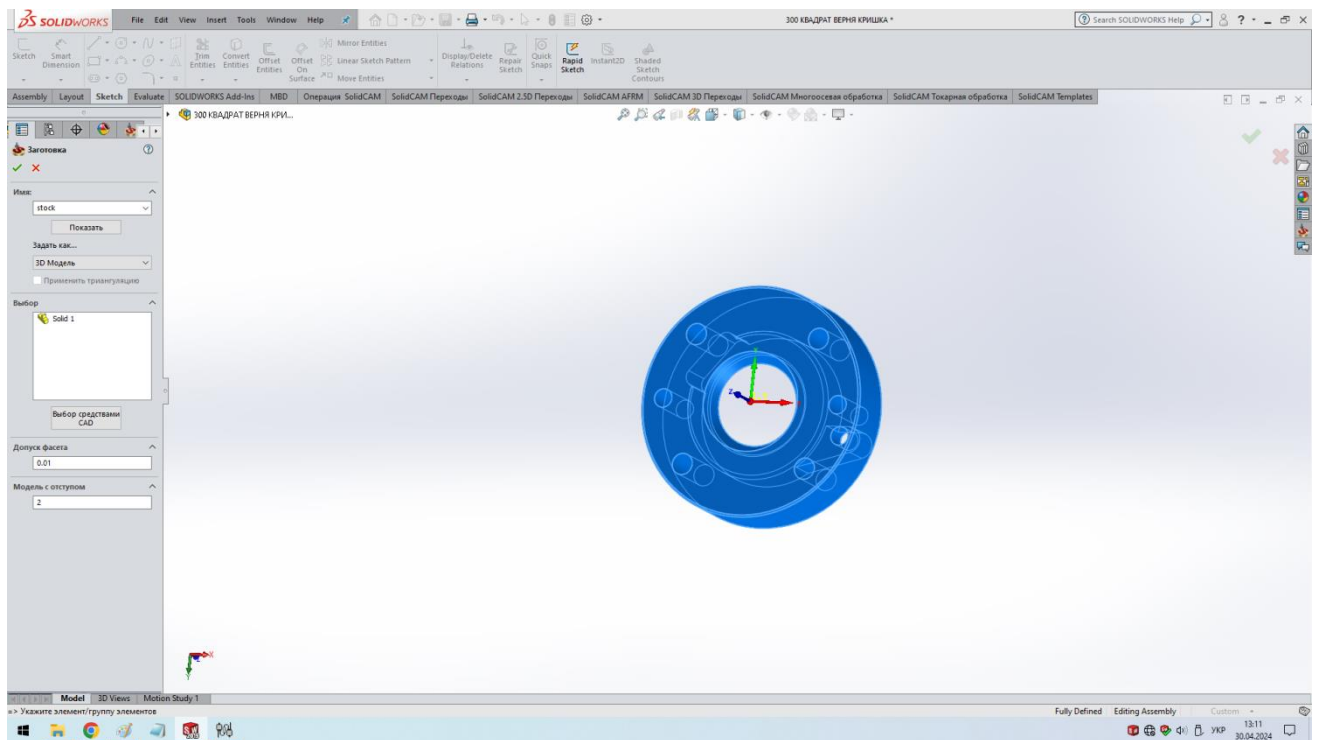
Створення заготовки деталі кришка у Solid CAM
